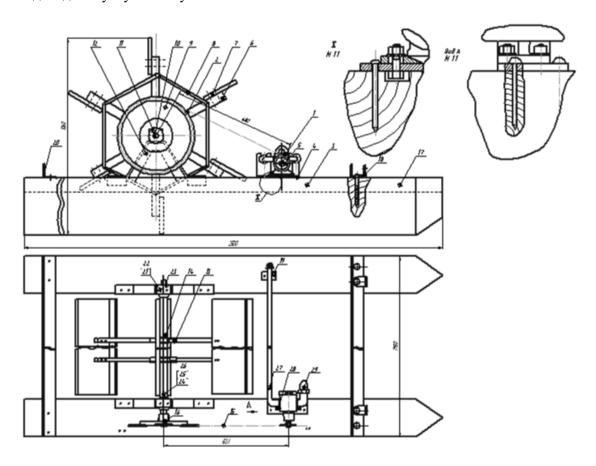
Плавающий насос: 1 — насос; 2 — колесо; 3 — плавающая платформа; 4 — плита установочная; 5 — звездочка; 6 — луч; 7 — лопасть; 8 — растяжка; 9 — звездочка; 10 — цапфа; 11 — подшипник; 12 — кронштейн; 13 — фланец; 14 — вал; 15 — цепь привода; 16 — ступица звездочки; 17 — пантон; 18 — проушина; 19 — кронштейн; 20 — уголок; 21, 24 — болты; 22, 25 — гайки; 23, 26, 28 — шайбы; 27, 29 — трубы
